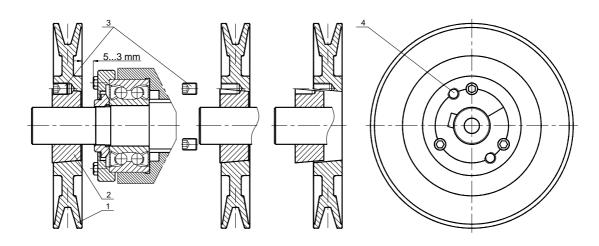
Порядок снятия шкива. 1– шкив; 2– втулка; 3– болт; 4– резьбовое отверстие для снятия шкива.
